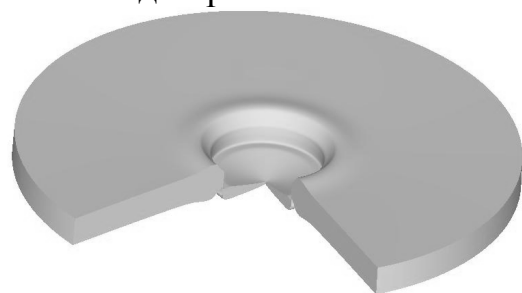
Заготовка в розрізі на завершених стадіях пробивання перемички
